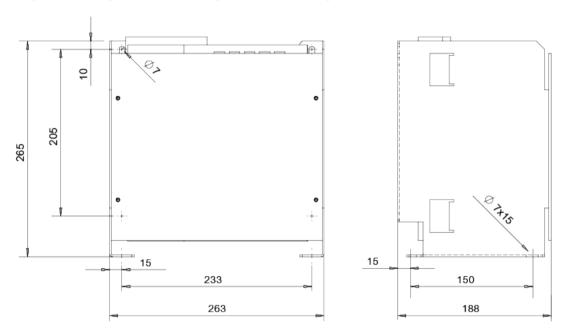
Габаритный чертеж схемы ограничения напряжения, тип 1
